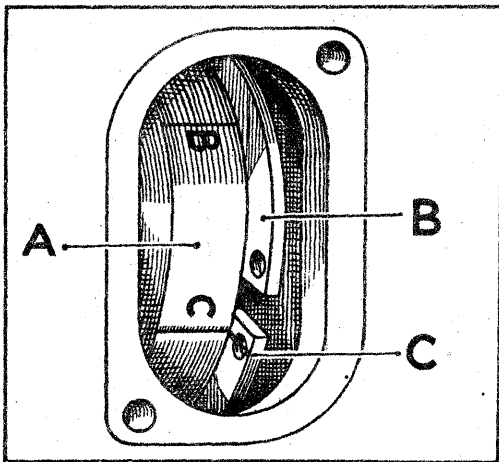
Indstillingsmærker på brændstofpumpens rotor.
